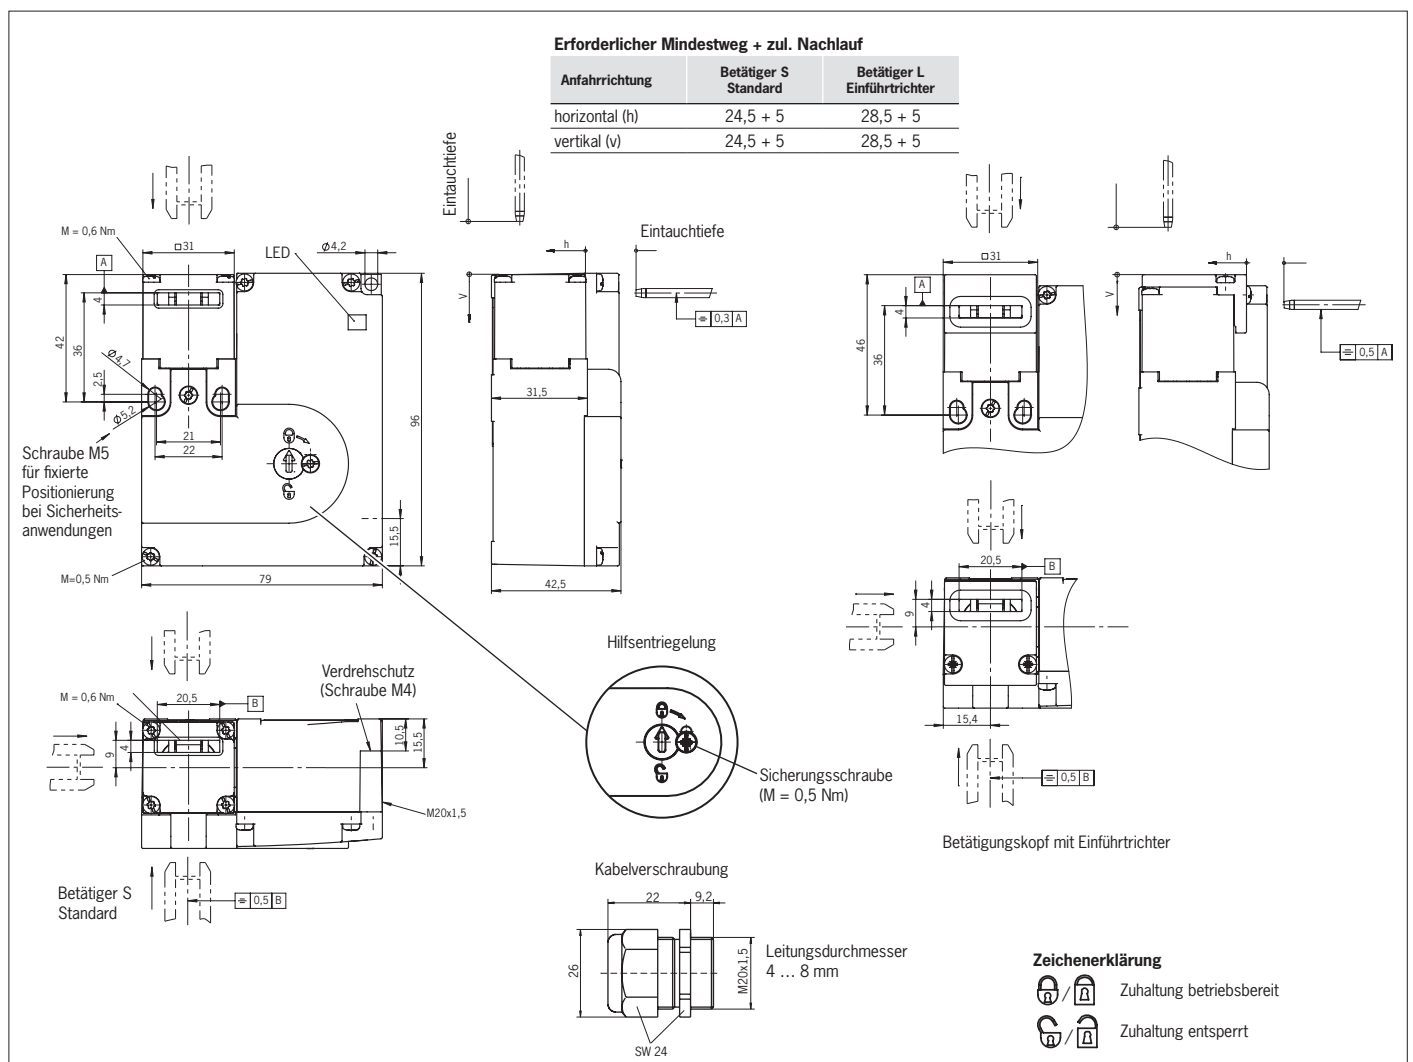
Maßzeichnung STM Pro ohne Einführtrichter und STM Pro mit Einführtrichter
